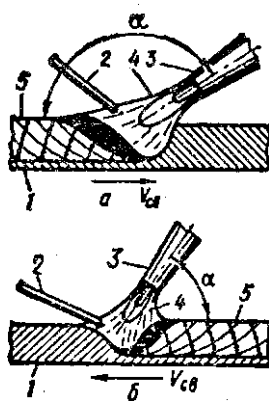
Схема газовой сварки: а — правым способом; б — левым
